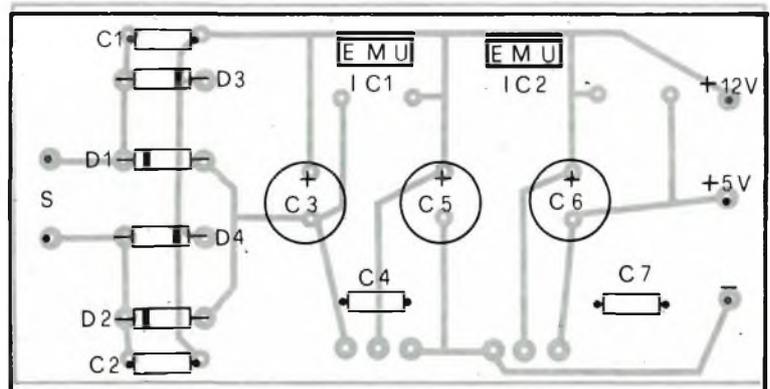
Basetta master vista dal lato componenti dell'alimentatore.
